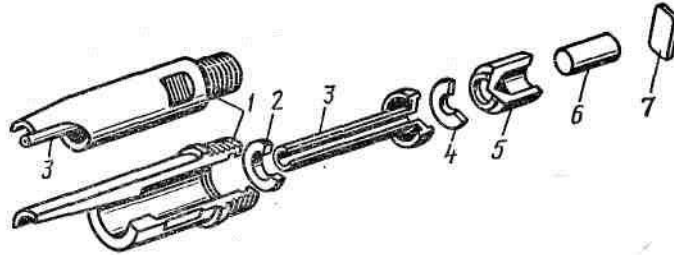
Соскова автопоїлка ПБС-1: 1 – корпус; 2, 4 – гумові прокладки; 3 – сосок; 5 – клапан; 6 – амортизатор; 7 – упор.
